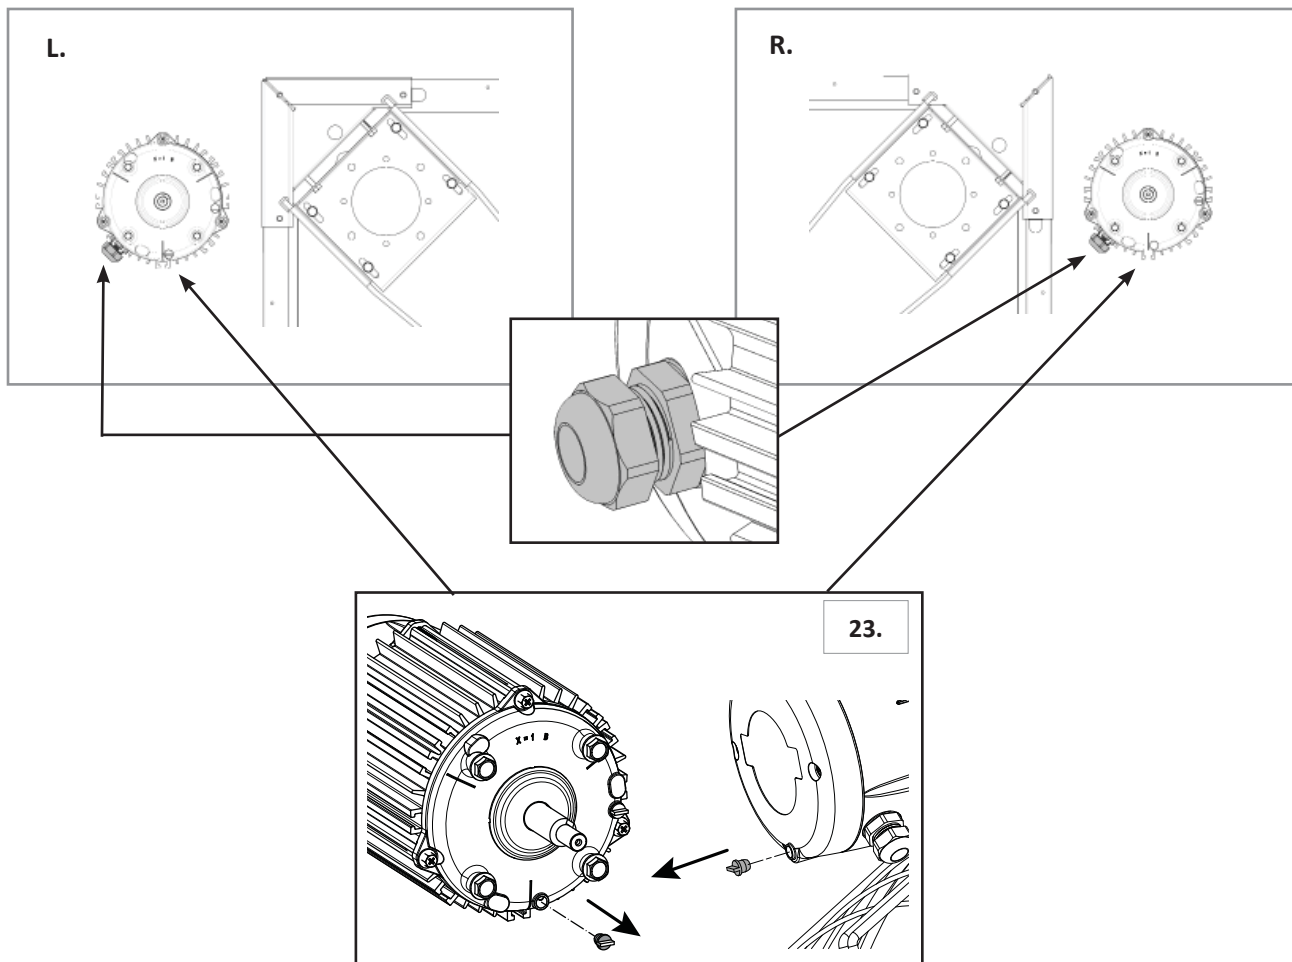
Fig. VII Montage / Assembly / Montage / Montage / Montaje / Сборка
